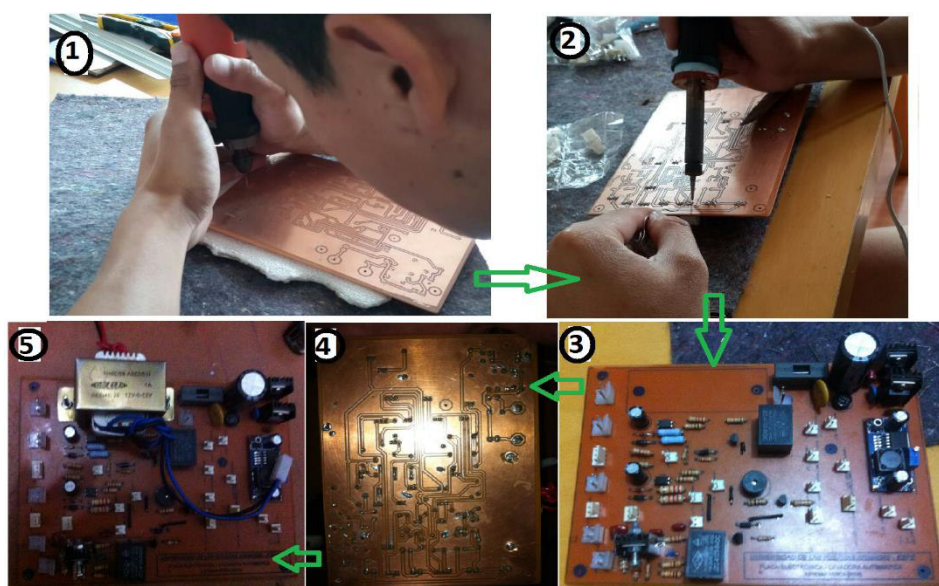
Perforación y soldadura de componentes en la PCB
